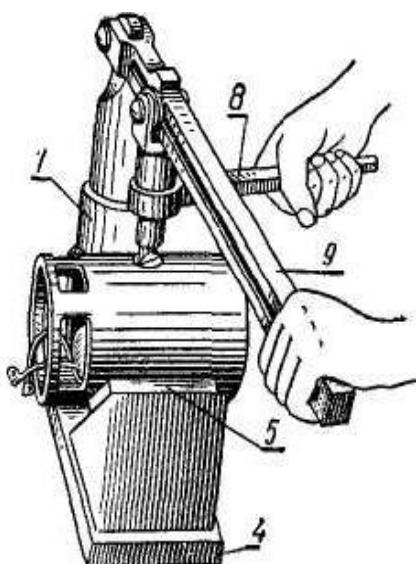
Рычажное устройство для вывертывания винтов
